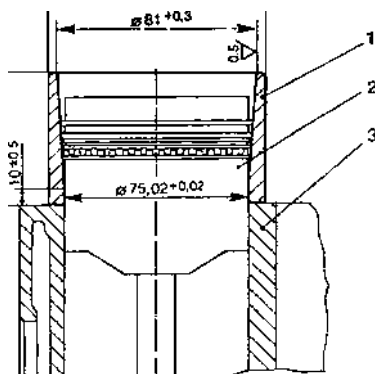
Оправка для установки поршня с кольцами и шатуном в цилиндр:
